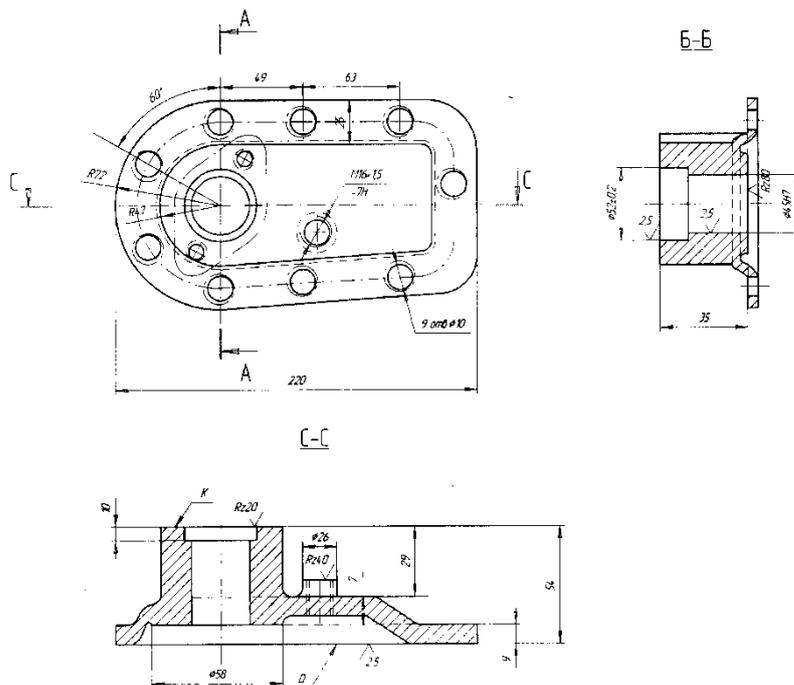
Чертеж крышки редуктора (отливка 3-го класса точности. Отклонение от плоскостности поверхностей К и Д не более 0,05 мм)
